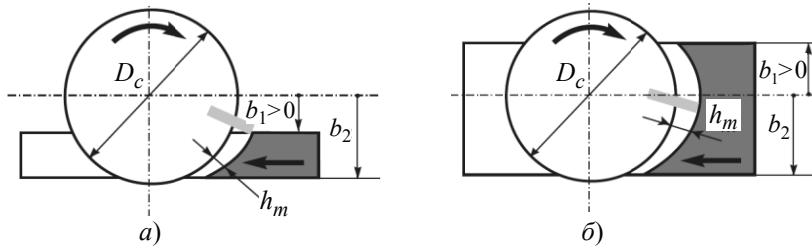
Расстояния от краев фрезерования до оси фрезы D_c , расположенной вне (а) и внутри (б) заготовки
